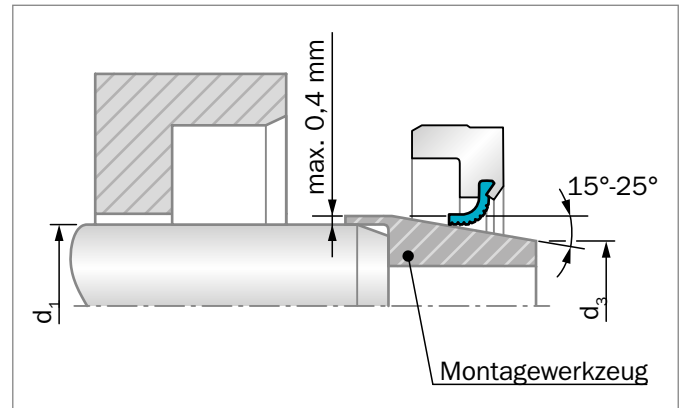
Montage der Dichtlippe mit einem Montagewerkzeug
